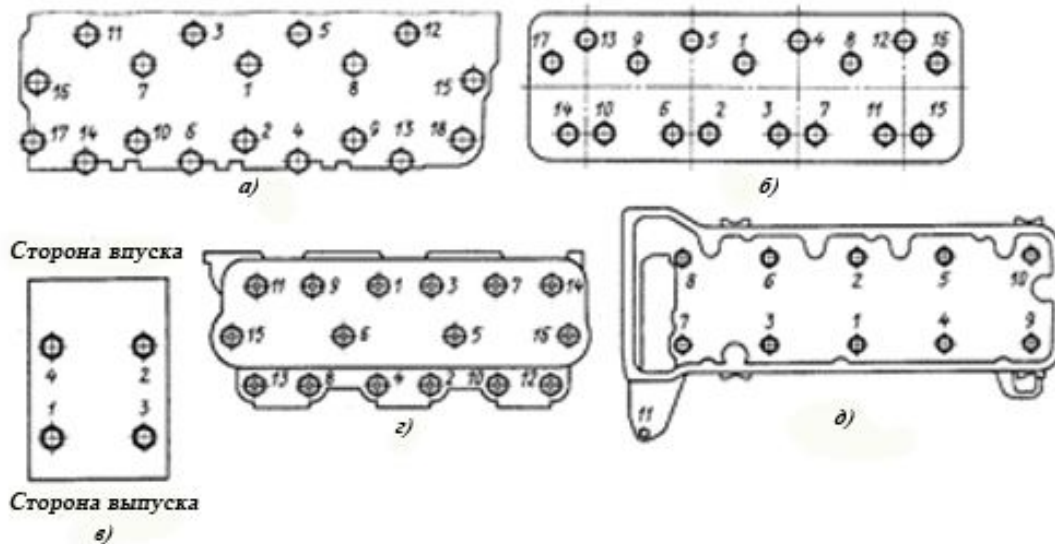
Порядок затяжки гаек или болтов крепления головки блока цилиндров двигателей автомобилей:
